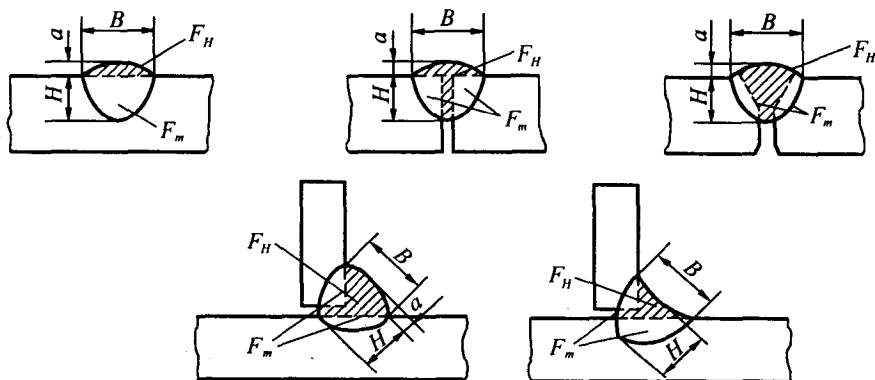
焊缝的形状和尺寸示意图
